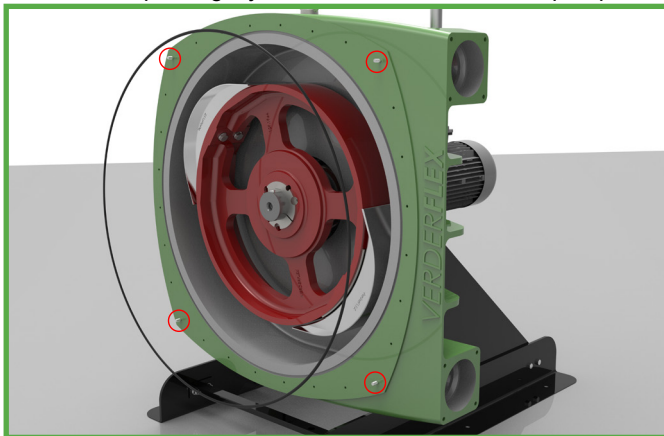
Insertion du joint torique (assemblage du couvercle avant)
